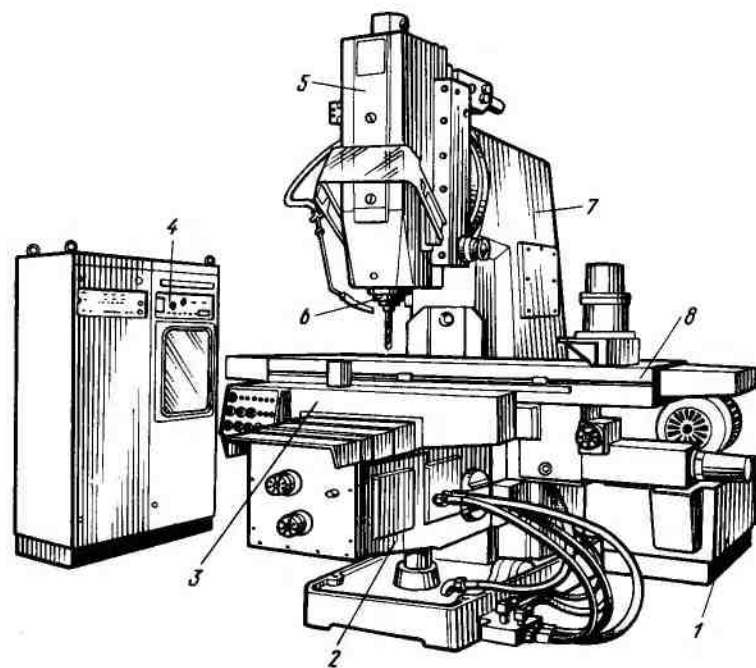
Фрезерный станок мод. 6Р13Ф3 с ЧПУ
